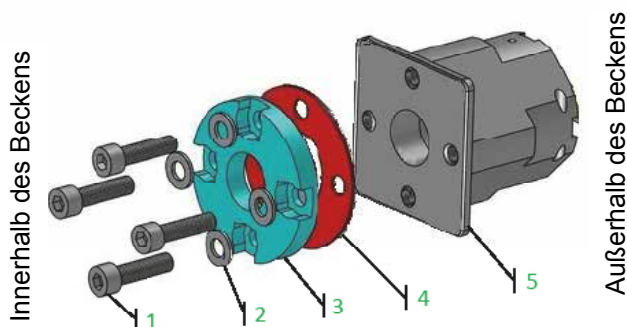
Montage des Flansches für die Wanddurchführung
